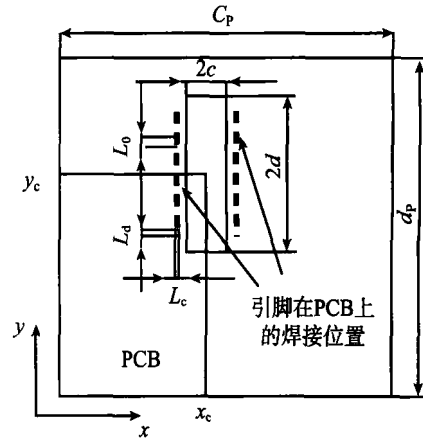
DIP 焊接在 PCB 上的位置及各器件尺寸
